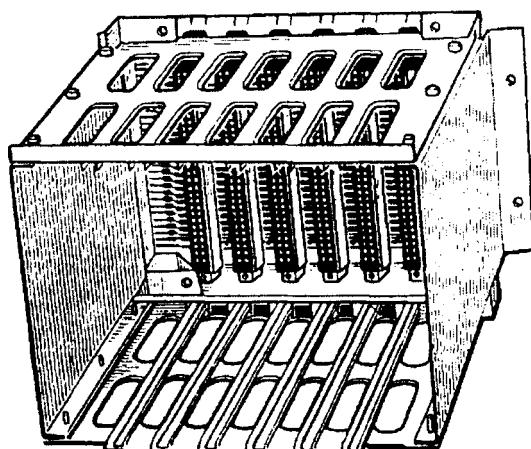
Общий вид несущей конструкции блока разъемного типа
